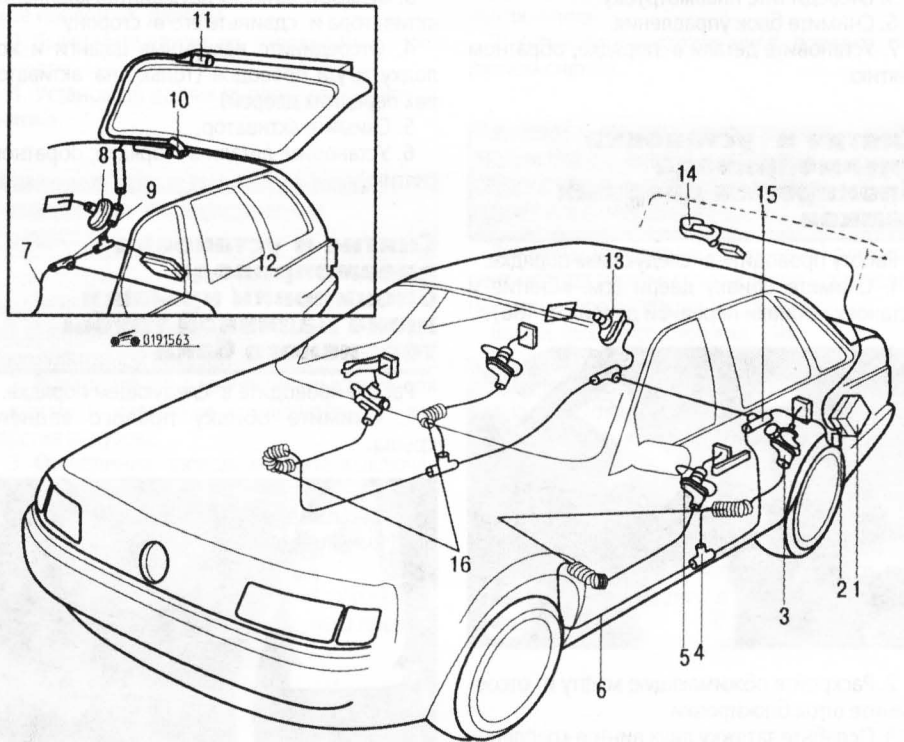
Устройство системы блокировки замков: 1, 12 – блоки управления; 2, 4, 9, 15 – тройники; 3 – активатор задней двери; 5 – активатор передней двери; 6 – пневмомагистраль; 7 – направление к активаторам дверей; 8 – активатор блокировки крышки люка наливной трубы топливного бака (автомобили с кузовом универсал); 10 – защитный чехол; 11 – активатор двери задка; 13 – активатор блокировки крышки люка наливной трубы топливного бака (автомобили с кузовом седан); 14 – активатор крышки багажника; 16 – защитные чехлы
